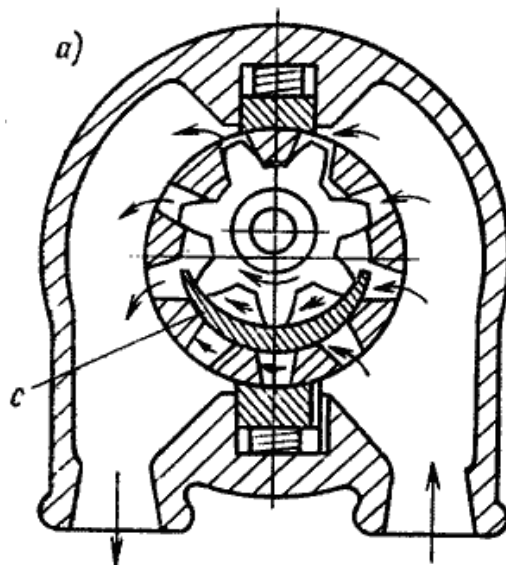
Шестеренный насос с внутренним зацеплением шестерен
